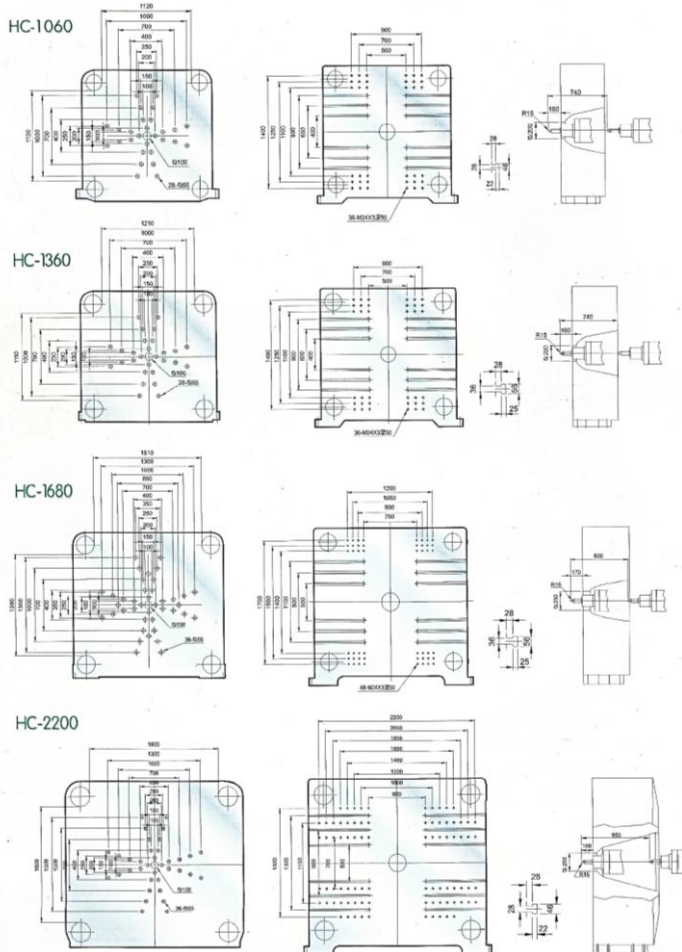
Dimensi *Mold Platen* unuk mesin injeksi merk *HWA CHIN MACHINERY FACTORY* bagian 3
